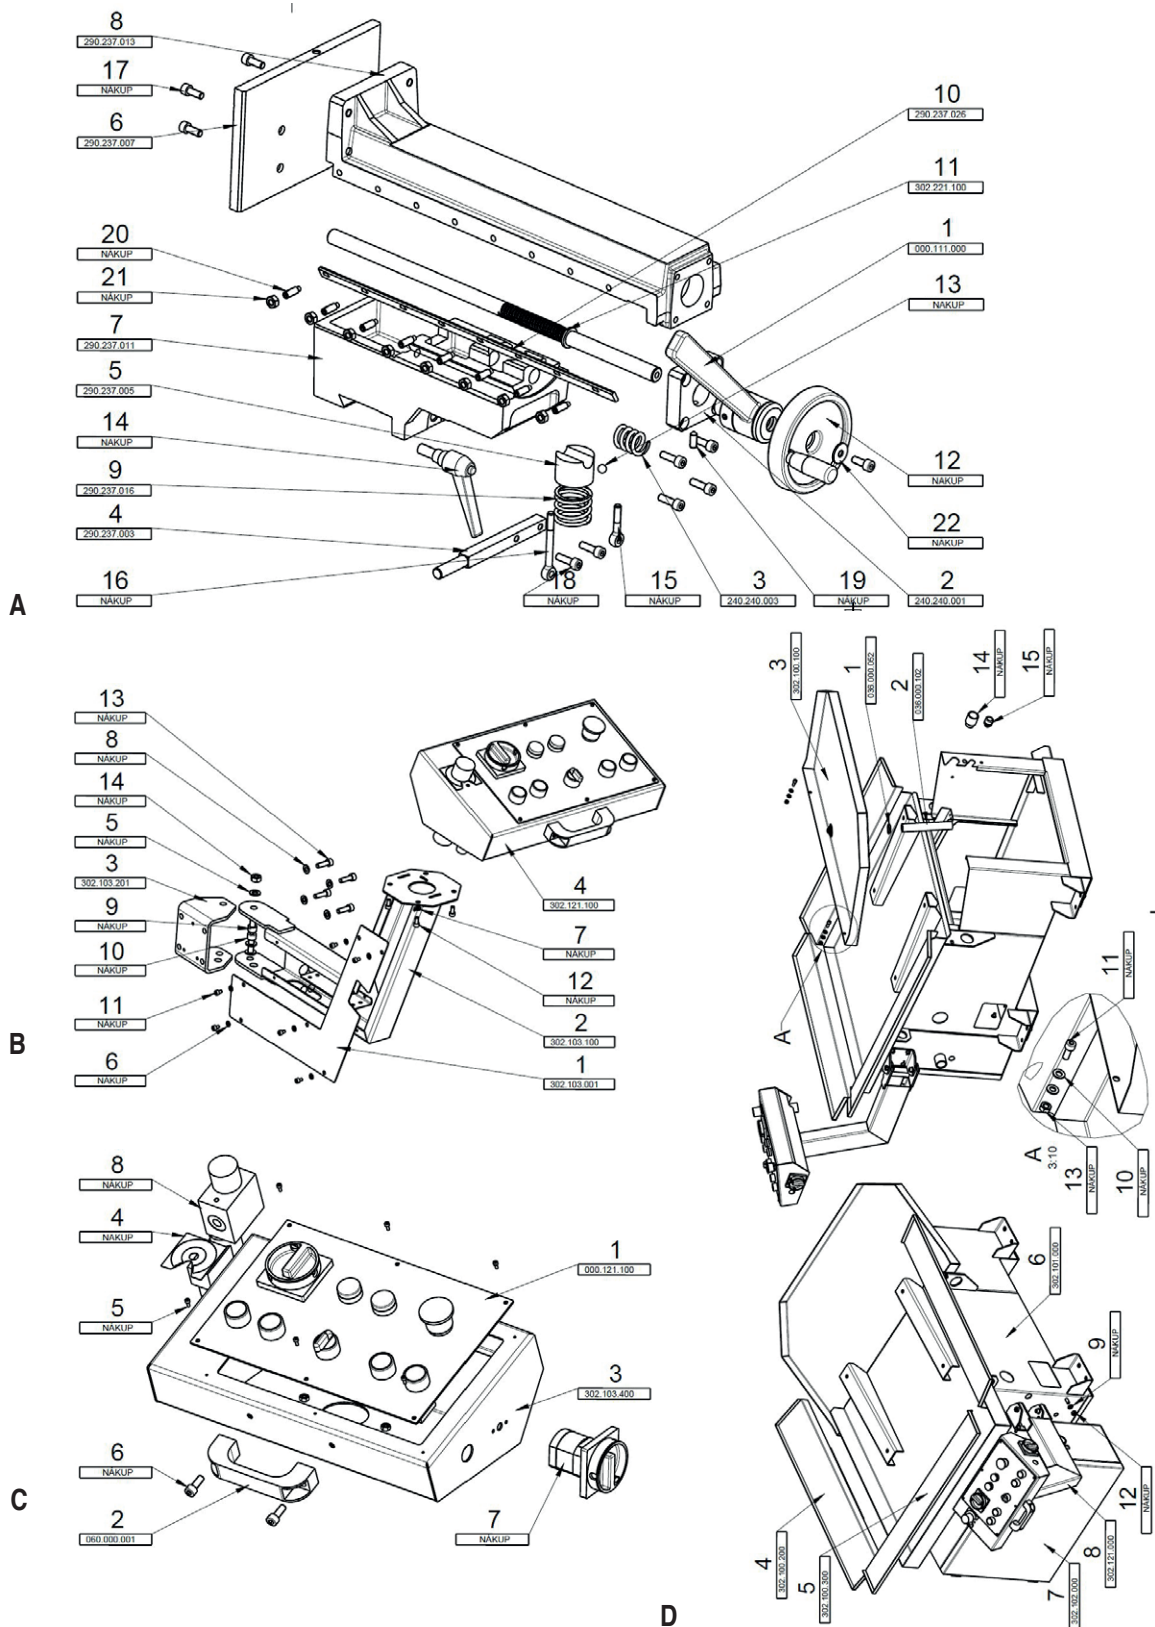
Onderdelentekening 3 - A : Spanklem, B : Bedieningspaneel houder, C : Bedieningspaneel, D : Frame
